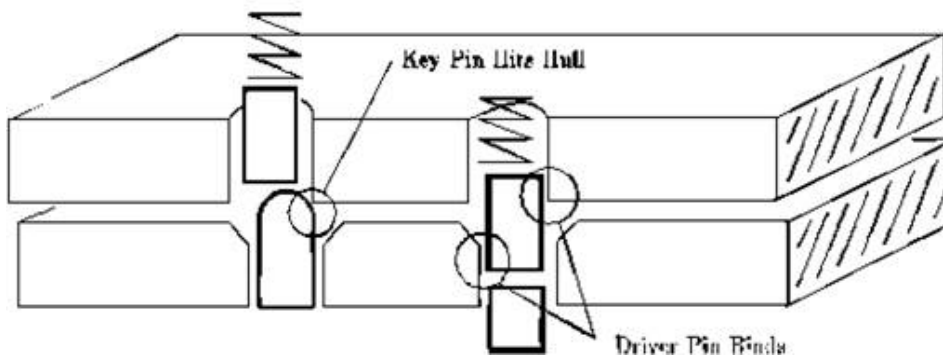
Зенкованные отверстия цилиндра и закругленные штифты
